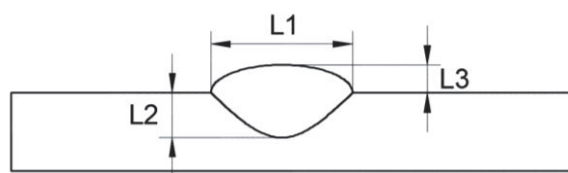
Dimensiones para macrografías de depósito de soldadura.
